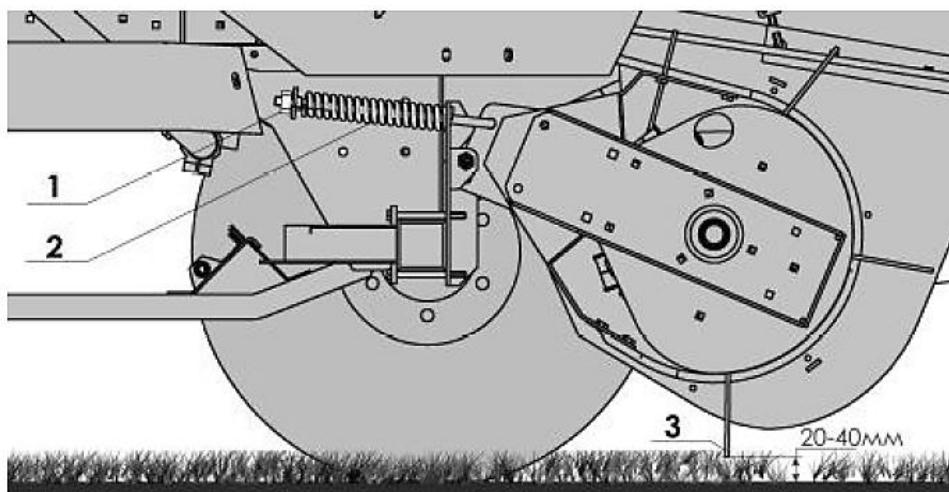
Установка подборщика: 1– гайка; 2 – пружина;
